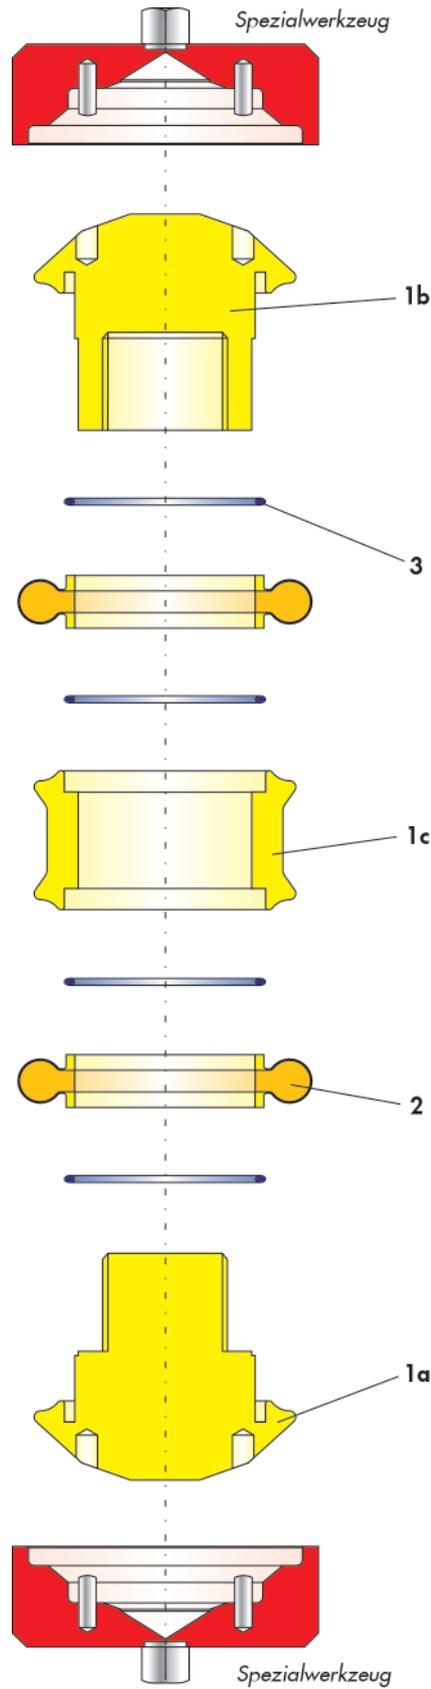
Explosionszeichnung des Molch TWIN 3
